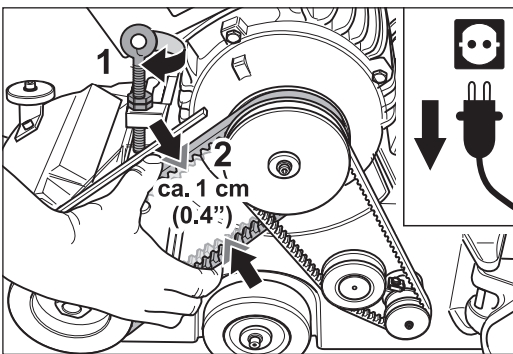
Zum Spannen des Antriebsriemens die Ringschraube am Motor im Uhrzeigersinn drehen (1). Richtige Spannung des Antriebsriemens: Der Keilriemen soll noch um ca. 1 cm zusammengedrückt werden können (2).
